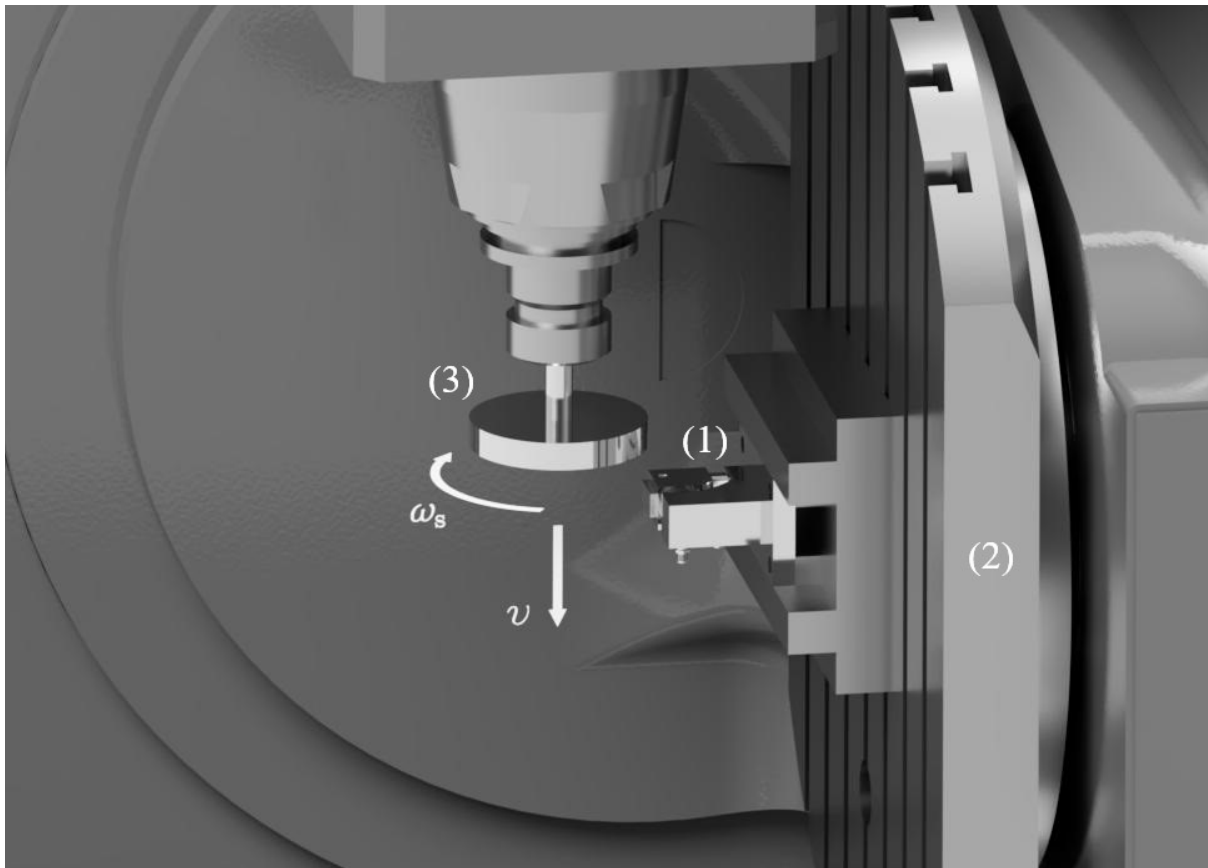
Composição do teste de riscamento de uma superfície metálica com único grão abrasivo. Fonte: Autor. Modelo tridimensional do centro de usinagem CNC disponível em <https://grabcad.com/library/dmu-50-2>, acessado em setembro de 2021.
